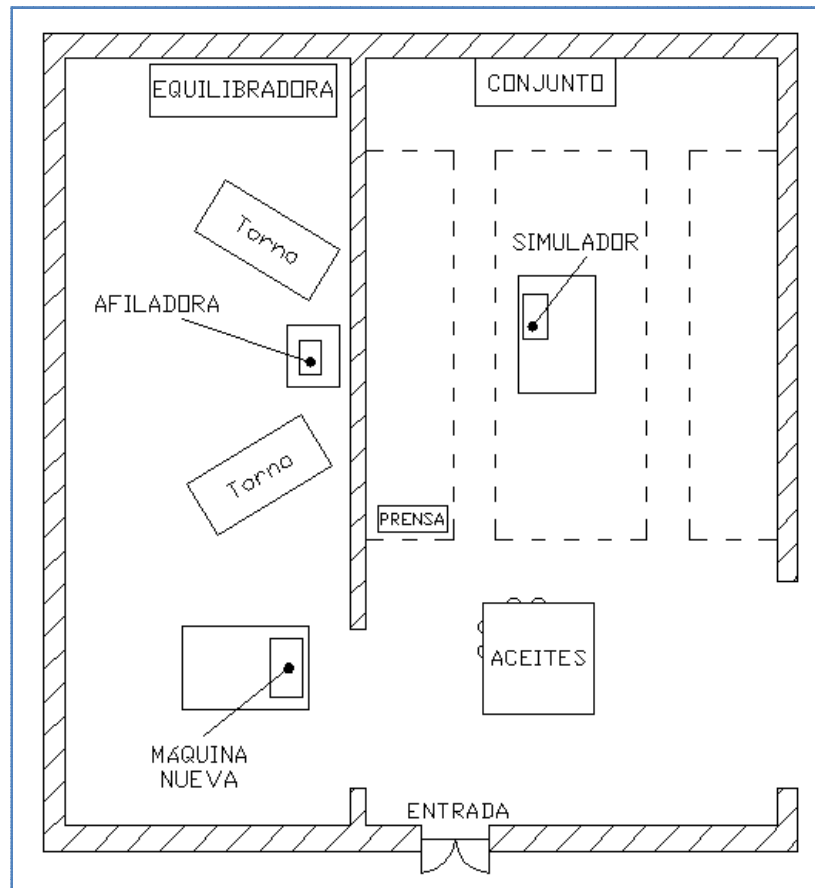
Croquis en planta de la 1ª distribución de zonas propuesta
